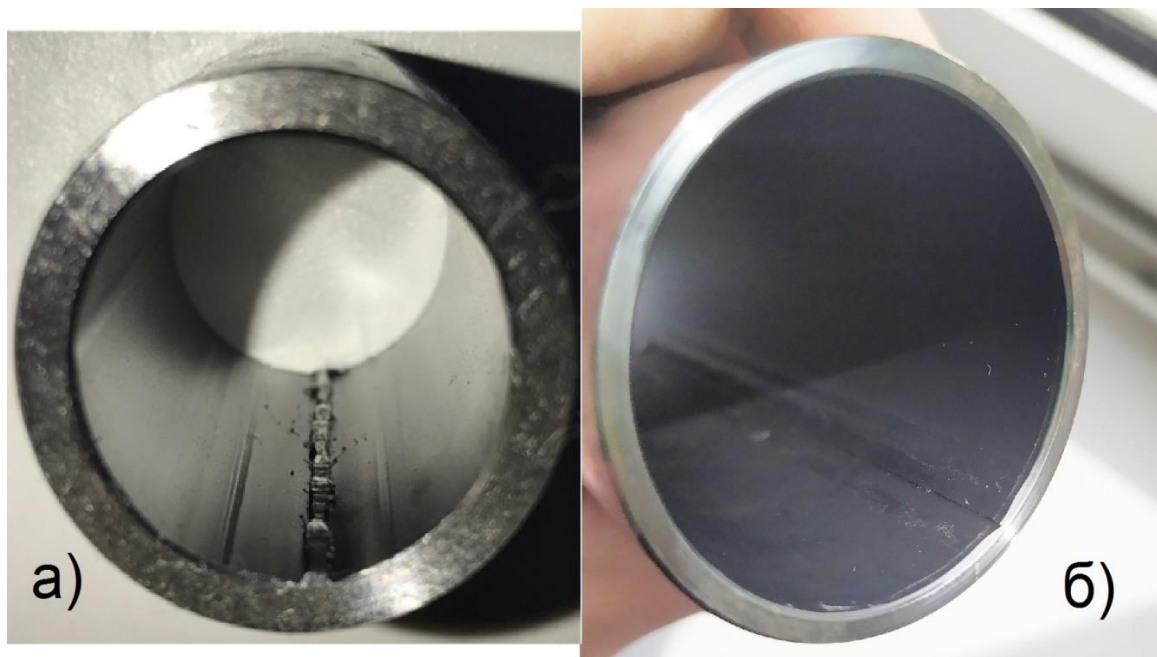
Трубная заготовка с внутренним сварочным гратом (а) и без грата (б)
